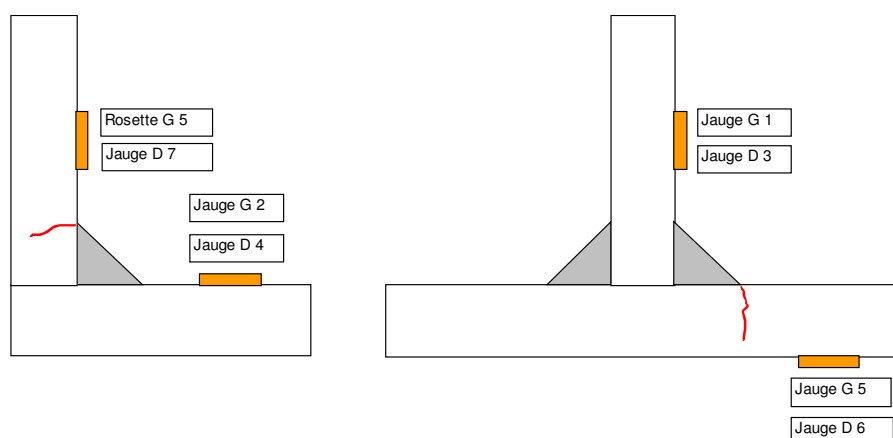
position de différentes jauges (soudure I à gauche et soudure II à droite).
